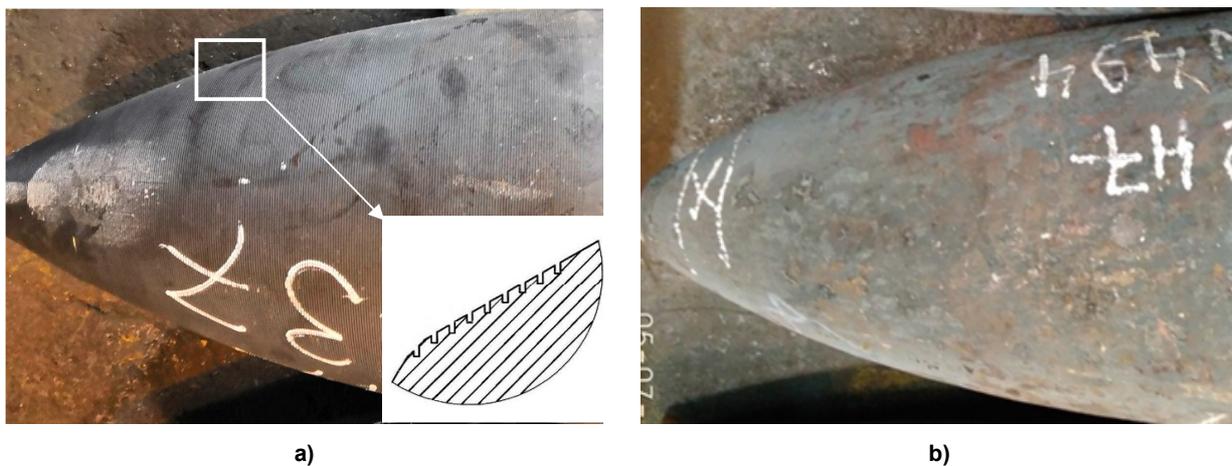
Внешний вид рабочей поверхности новой оправки: а) с рифлением на рабочей поверхности; б) без рифления
